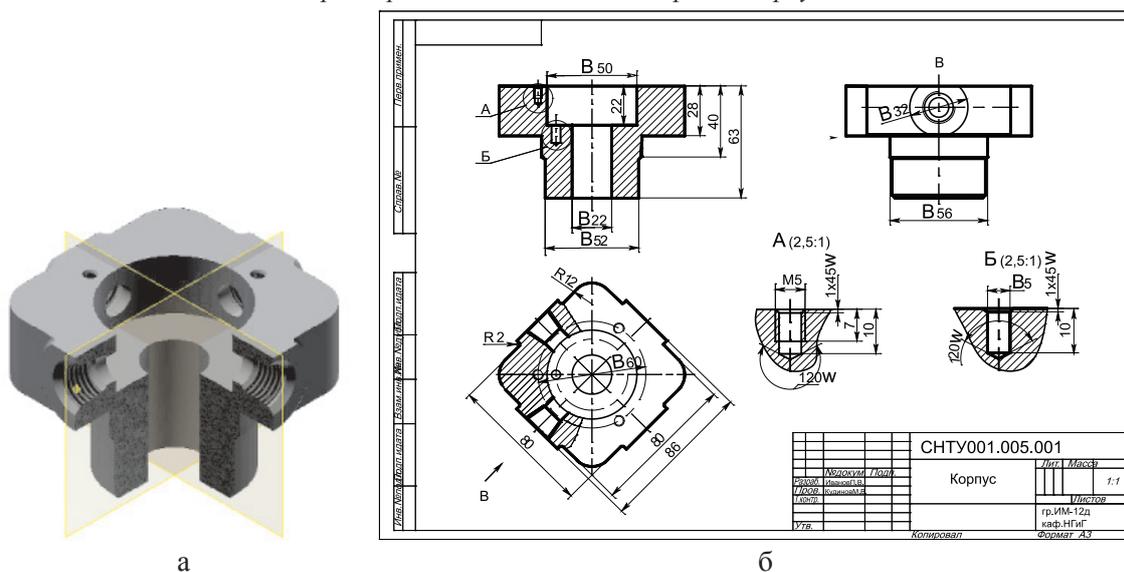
Трехмерная модель и плоский чертеж детали типа Корпус
